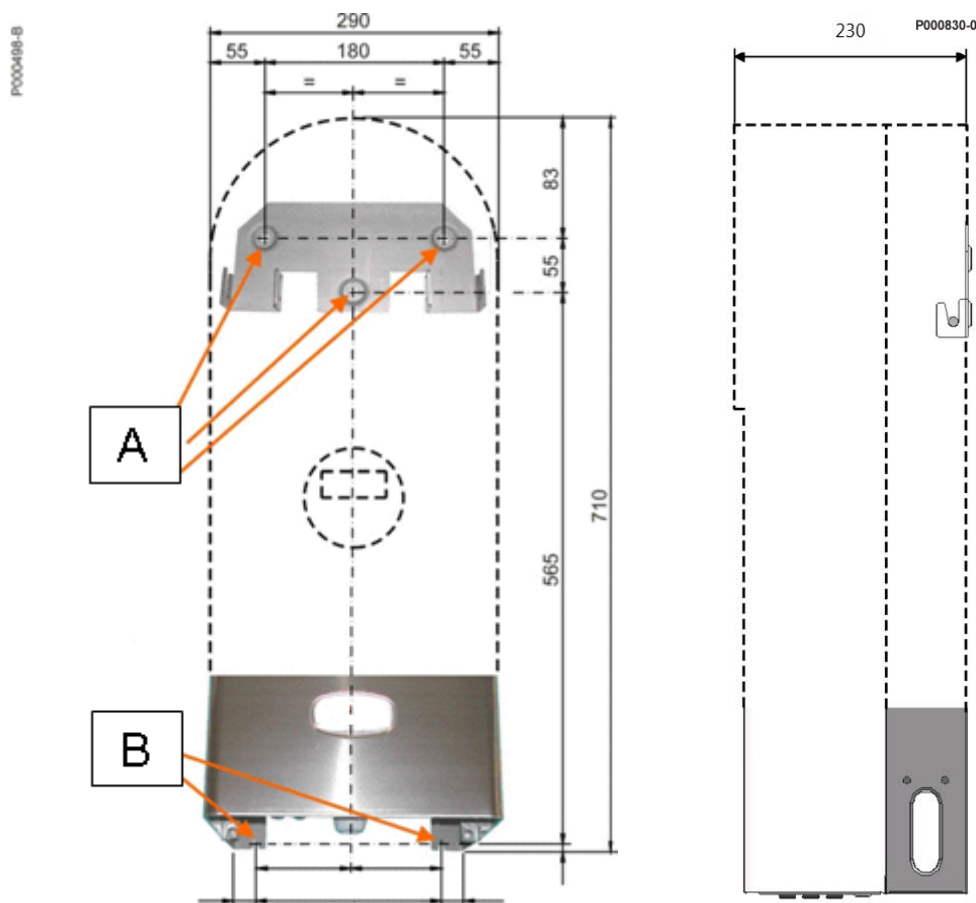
Particolare staffa Sunway M Plus con le viti di fissaggio
